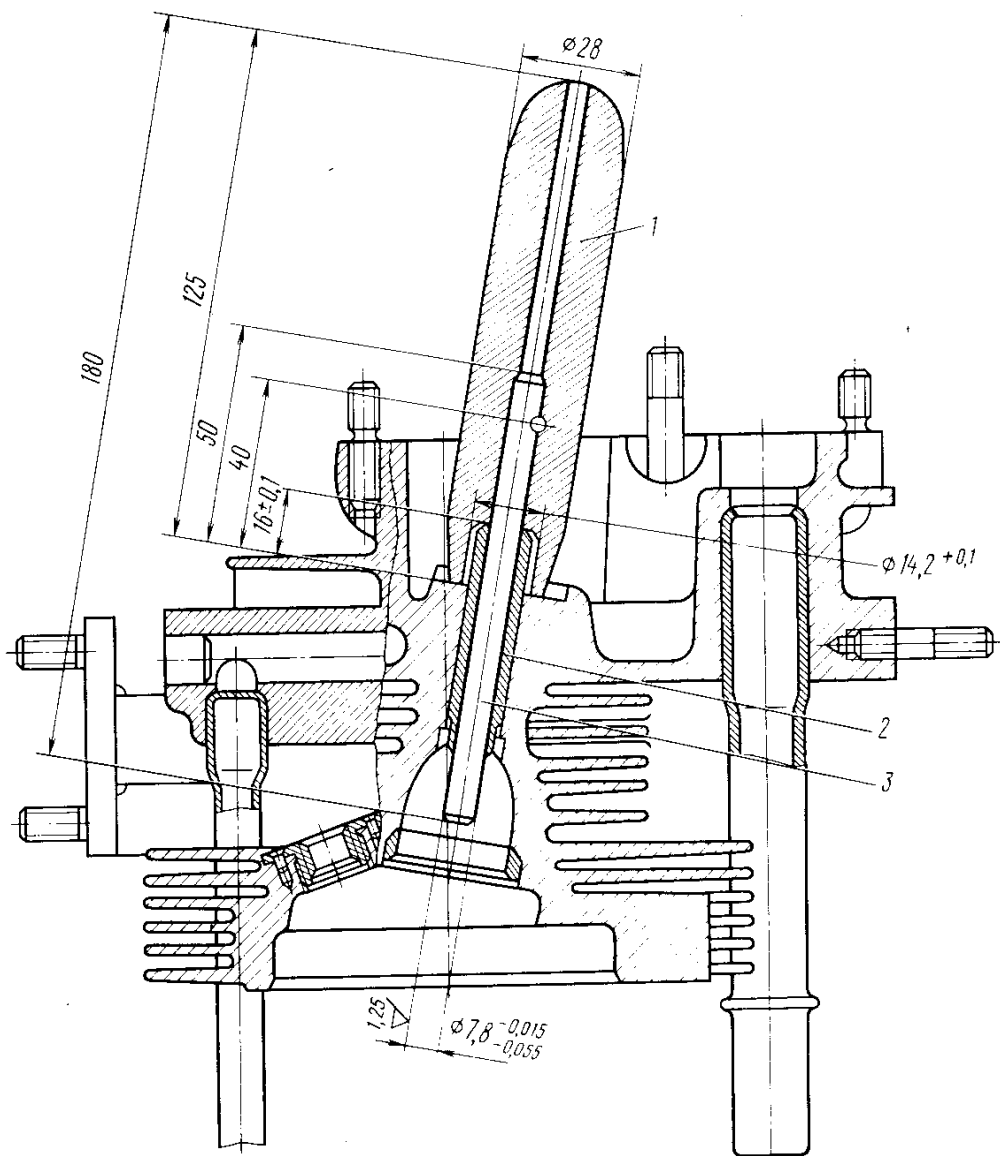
Оправка для запрессовки направляющих втулок клапанов: 1 — оправка; 2 — направляющая втулка клапана; 3 — направляющий штифт.
